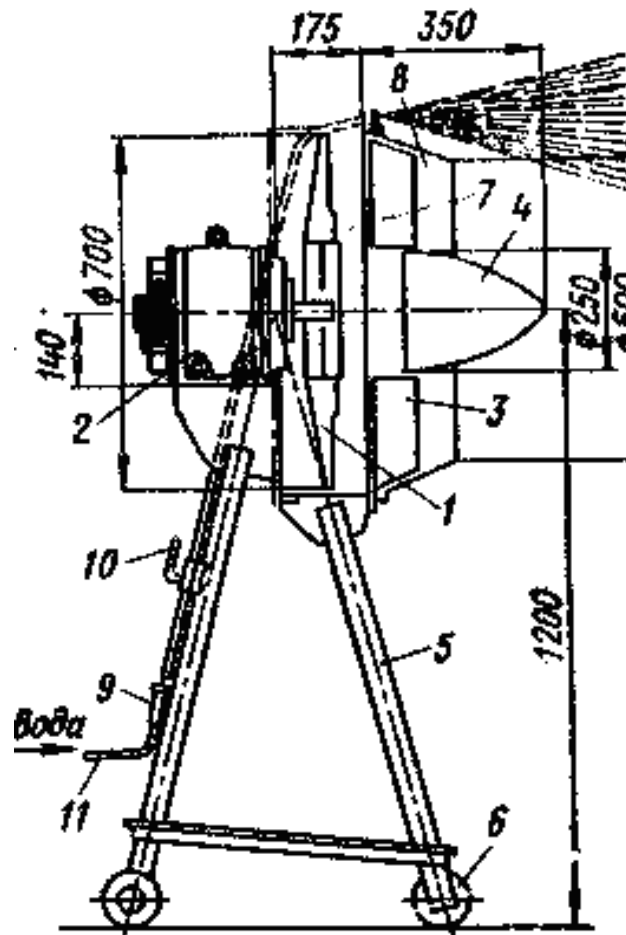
Душ конструкції СІОТ [40]: 1 – осьовий вентилятор; 2 – електродвигун; 3 – лопатка для вирівнювання повітряного потоку; 4 – обтічник (параболічної форми); 5 – металева конструкція; 6 – колеса; 7 – обичайка; 8 – захисна сітка; 9 – фільтр; 10 – кран; 11 – водовідвідні трубки
